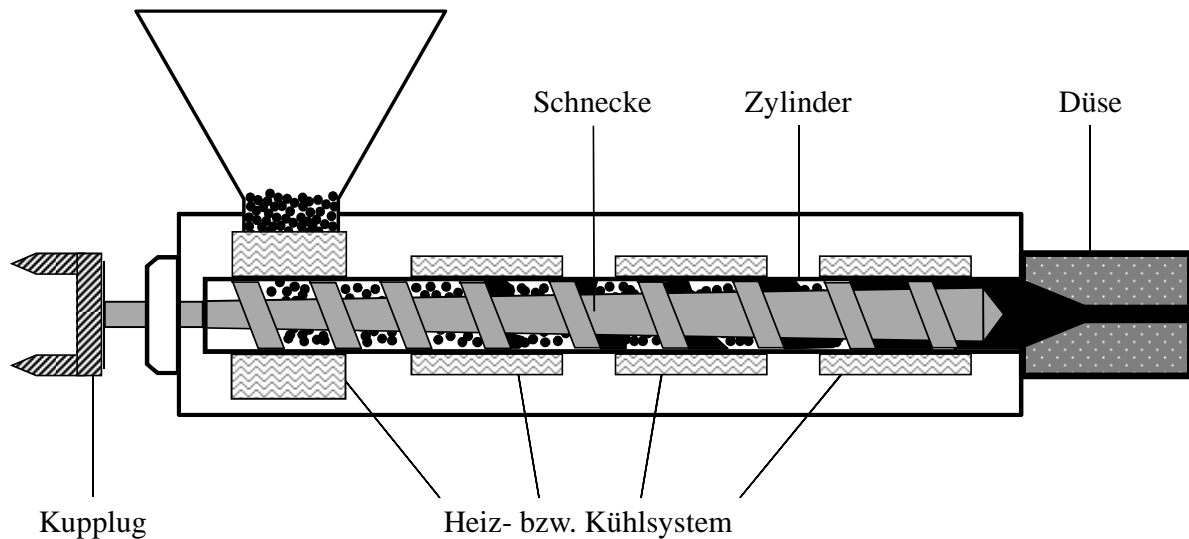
Schemazeichnung eines Einschneckenextruders (Thermo Fisher Scientific)
